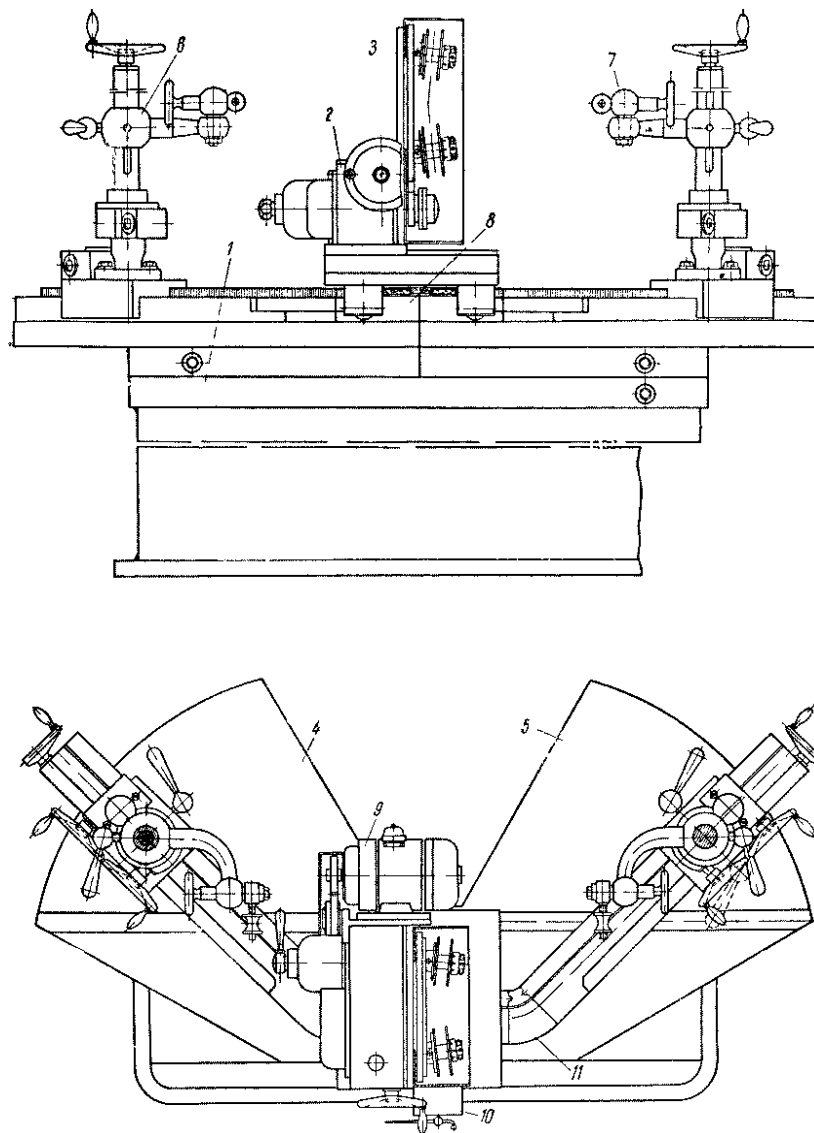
Универсальный изолировочный станок ЛУС–8 для статорных обмоток катушечного типа.
